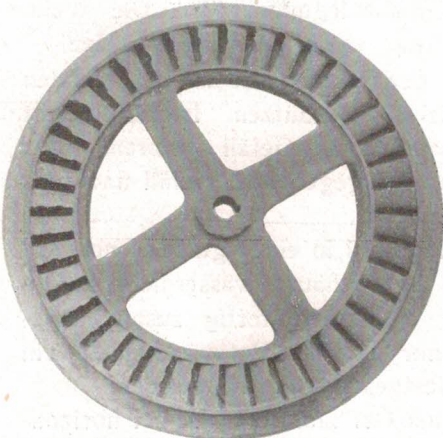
Laufrad einer Girard-Niederdruckturbine. Seite des Wassereintrittes.
